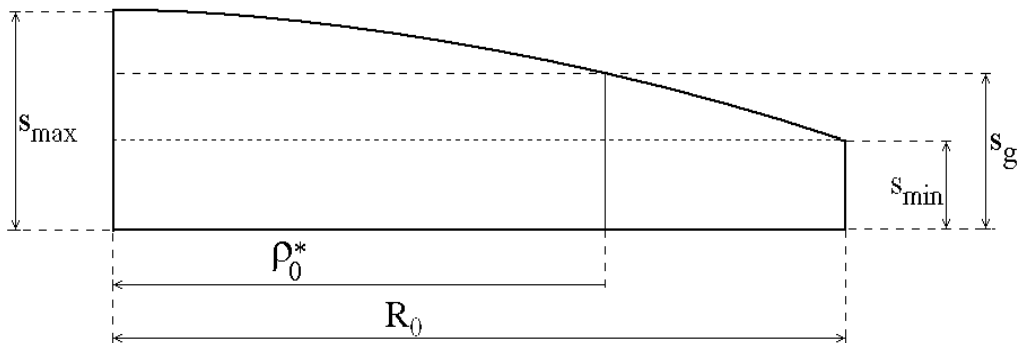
Геометрия заготовки формы шаровой сегмент
